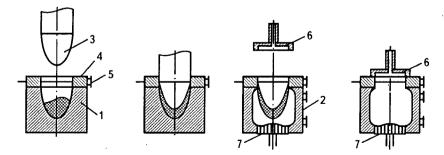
Схема прессовыдувания: 1 – черновая форма; 2 – чистовая форма; 3 – пуансон; 4 – горловые щипцы; 5 – шарнир; 6 – дутьевая головка; 7 – дно чистовой формы
